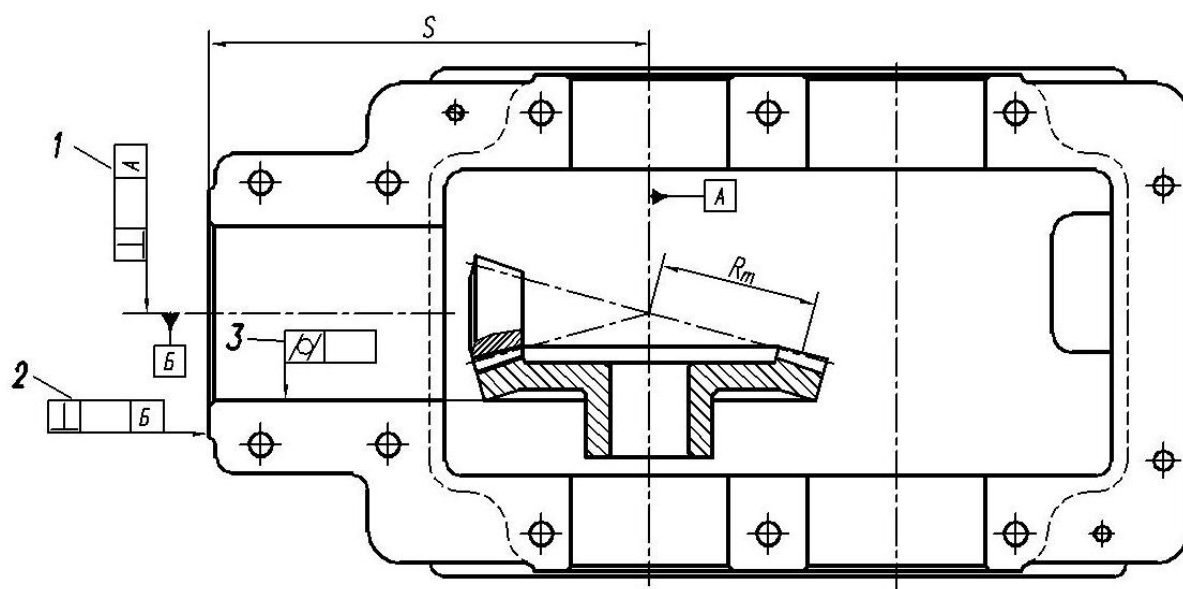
Размещение обозначений допусков форм и расположения поверхностей на чертеже основания корпуса коническо-цилиндрического редуктора
